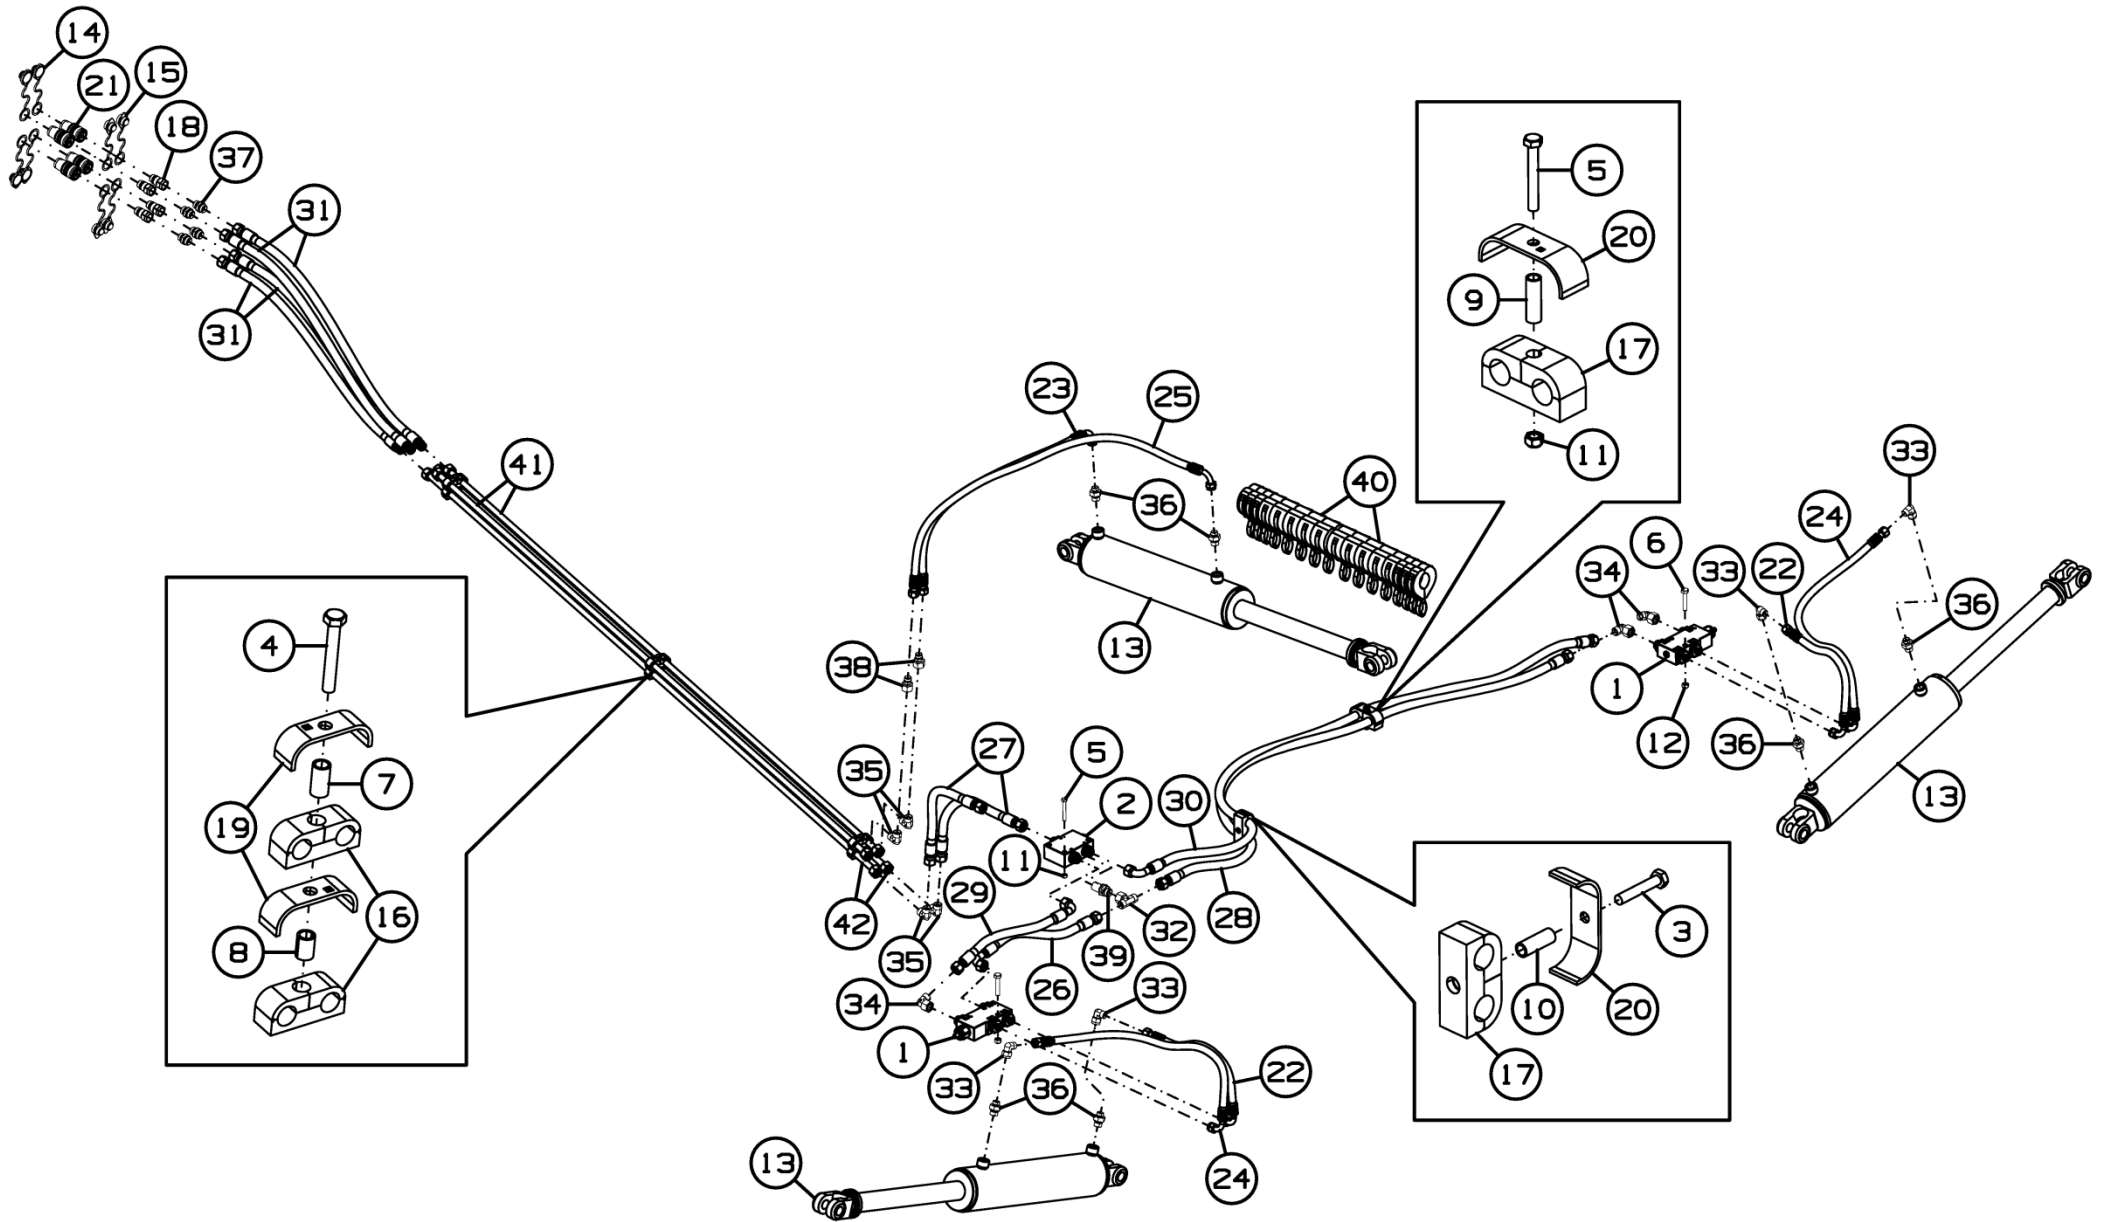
Установка гидрооборудования К-082.12.000А
